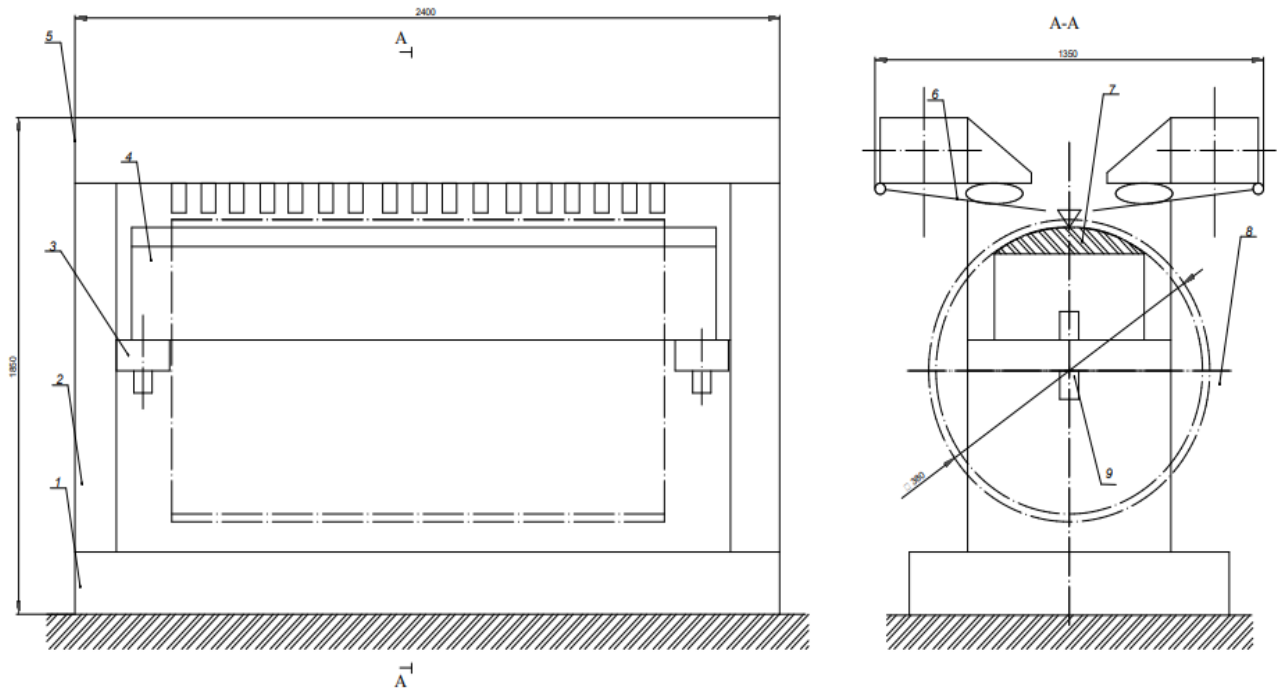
Затискний пристрій для складання та зварювання повздовжніх швів обичайок: 1 – рама; 2 – стояк; 3 – притискач; 4 – металева підкладка; 5 – верхня опорна балка; 6 – направляюча; 7 – планка; 8 – обичайка; 9 – шкворінь
